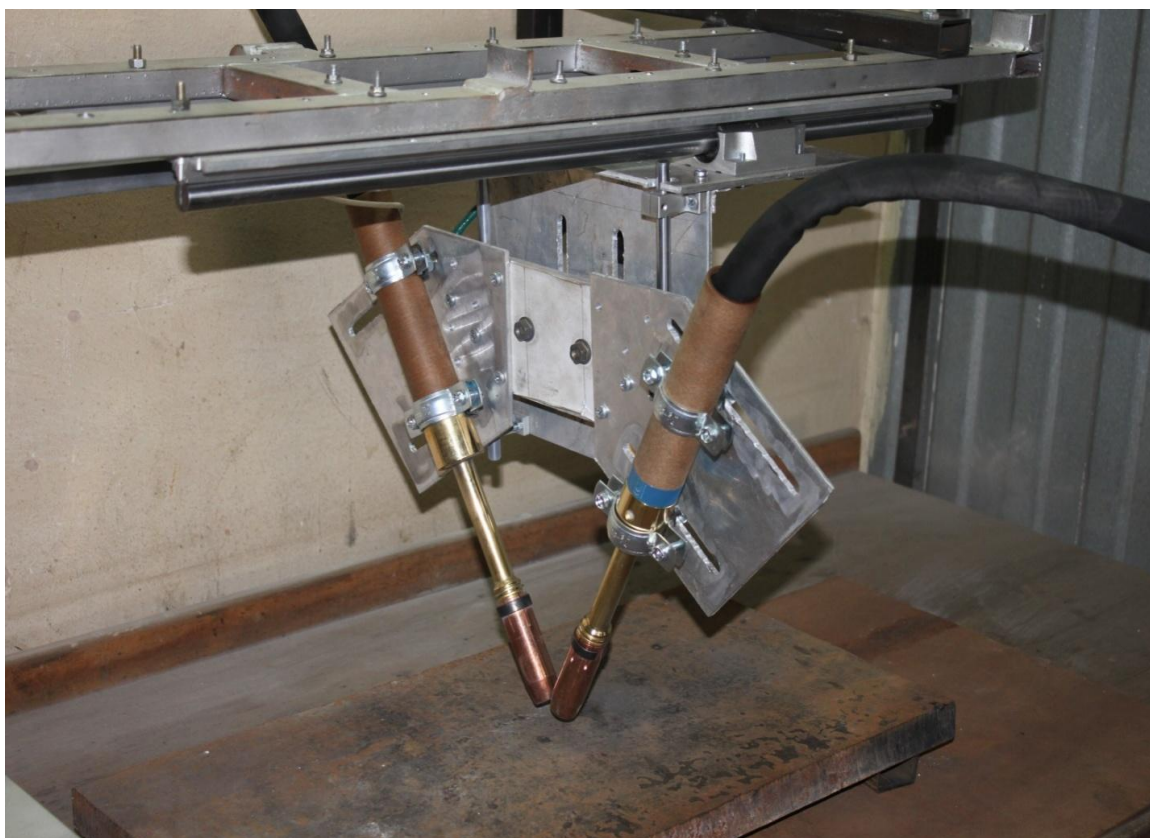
Установка для автоматической наплавки комбинацией дуг
